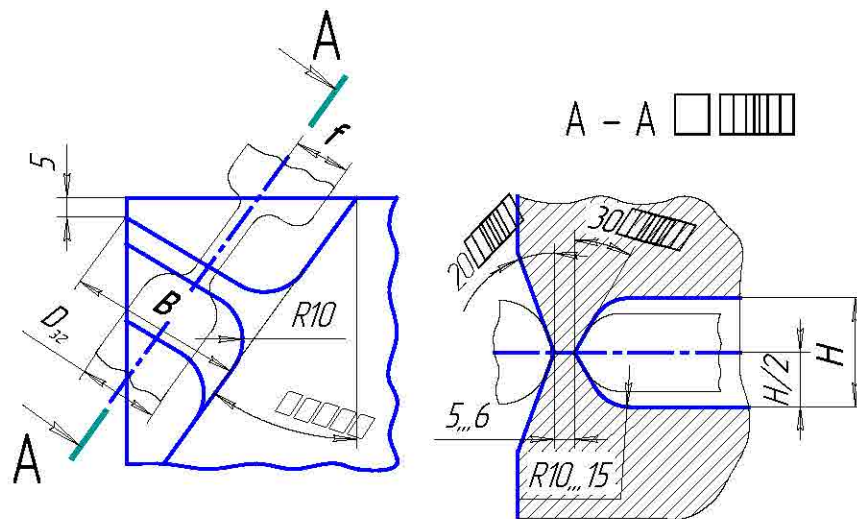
Ніж для відрубування заготовки від прутка
